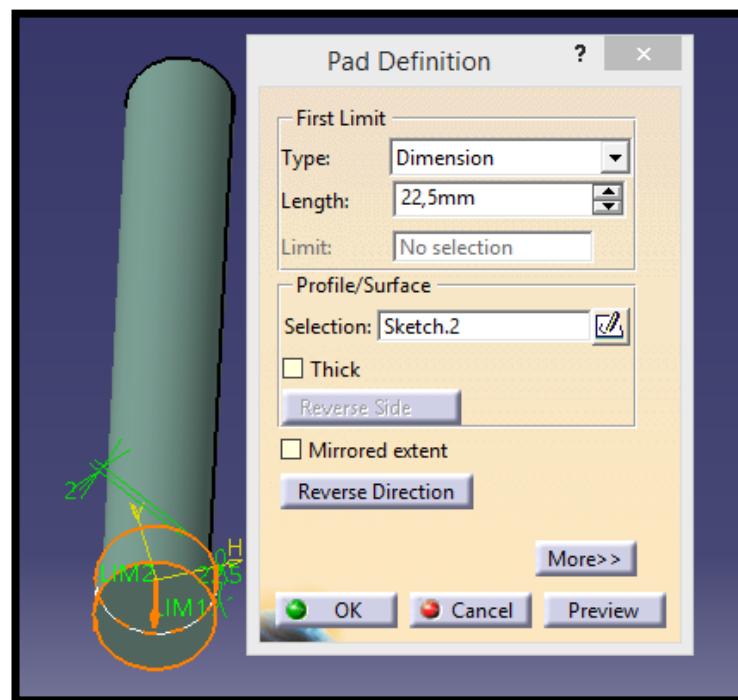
Seat mounting frame 11: Pad.2 barra inferior 2
